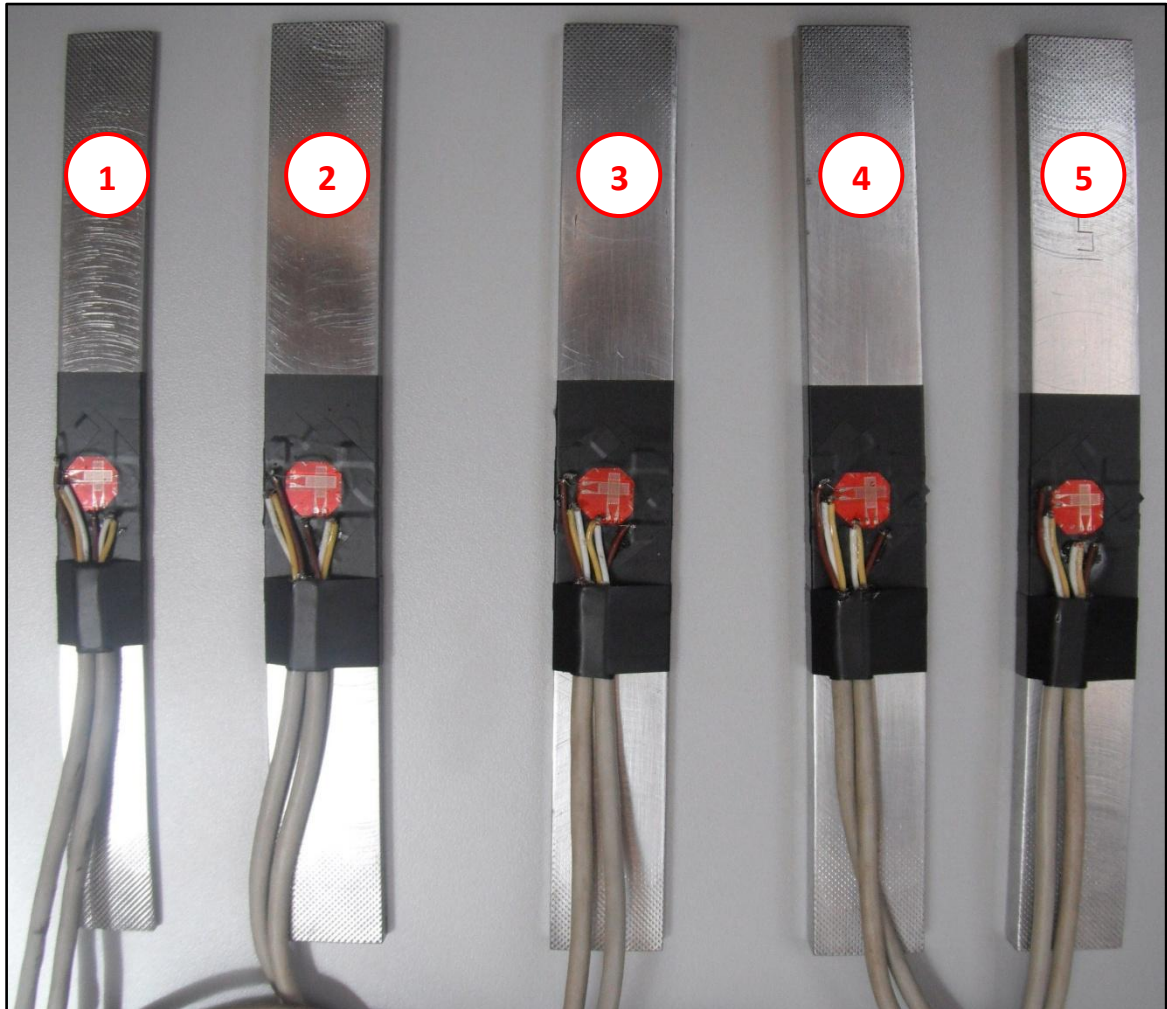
Probetas planas con las rosetas adheridas a su superficie
